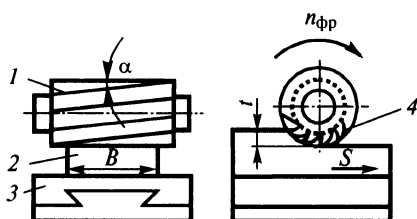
Схема фрезерования цилиндрической фрезой с винтовым зубом
